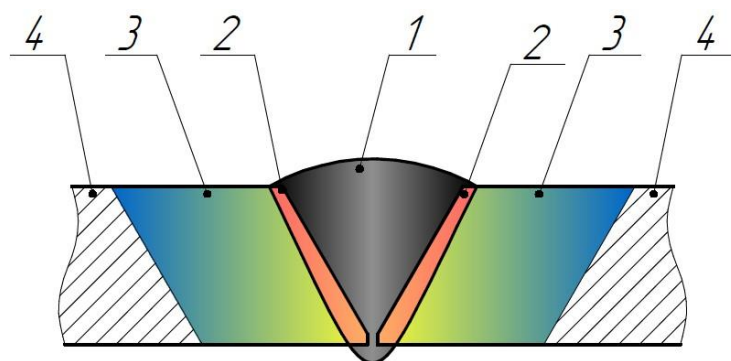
Схема разделения сварного шва на участки
